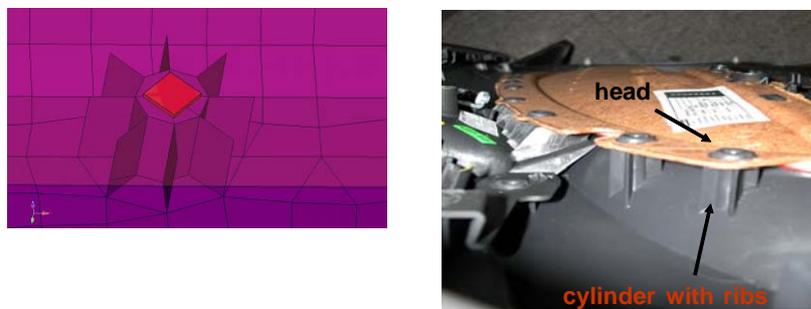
Modellierung einer Ultraschallverschweißung
